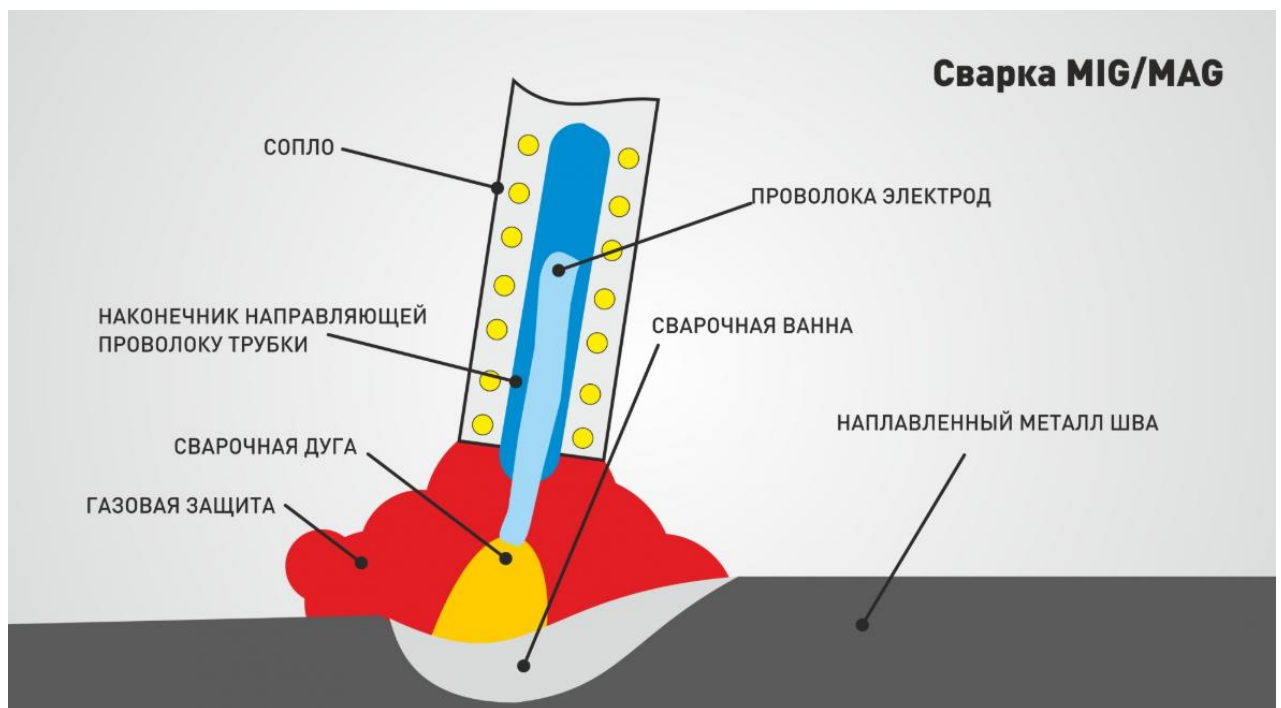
MIG/MAG зварювання. Ресурс [39]
